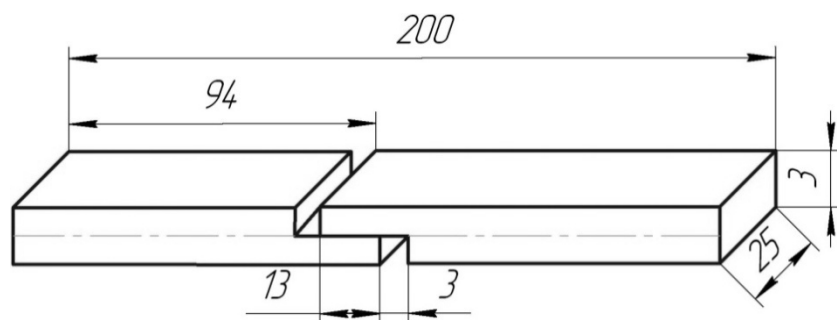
Образец для испытаний на межслойный сдвиг
